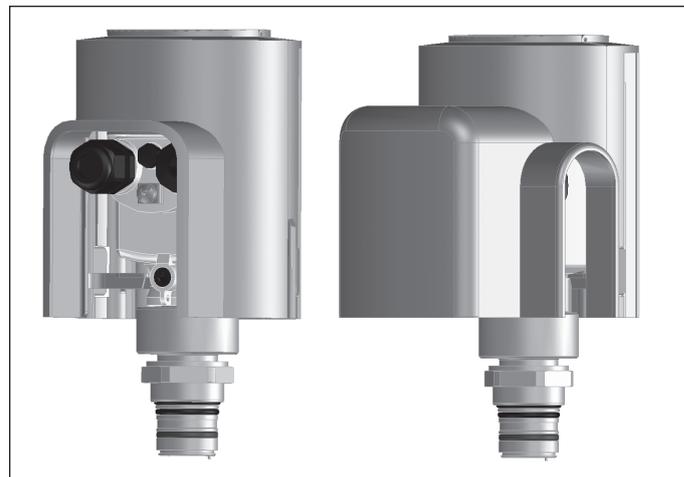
Wetterschutzhaube in verschiedenen Ausführungen
